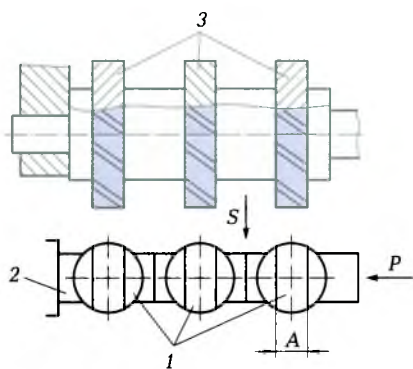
Схема одновременной последовательной обработки заготовки: 1 — режущий инструмент; 2 — заготовки; 3 — приспособление
